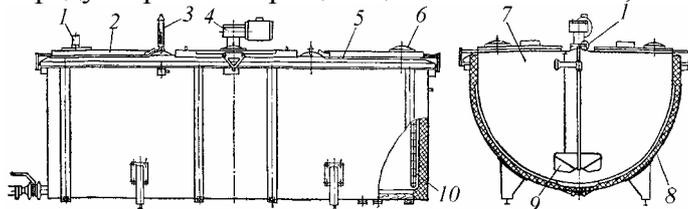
Резервуар промежуточного хранения типа РПО:
